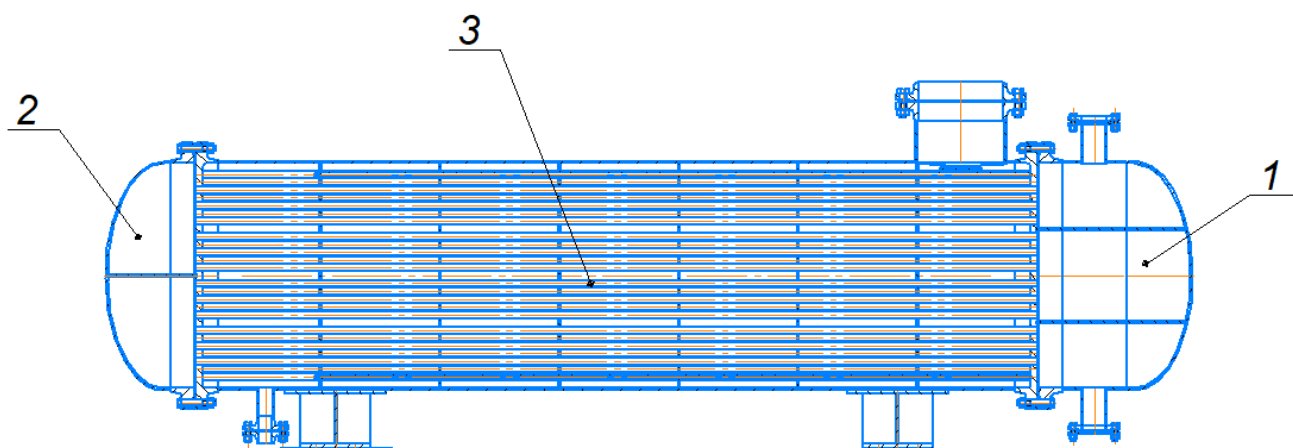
Схема чотирьох ходового кожухотрубного конденсатора:
